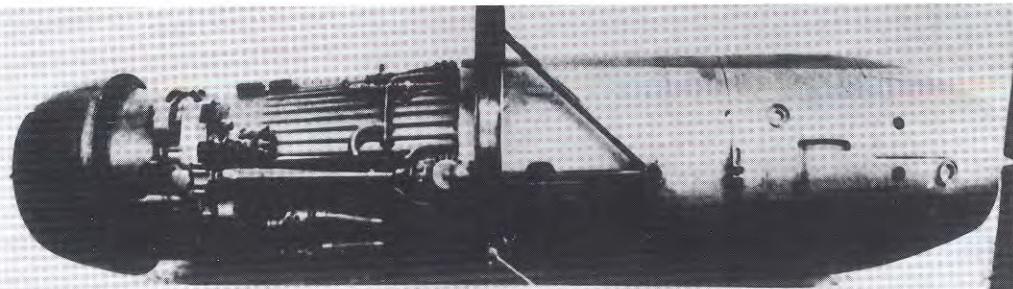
Турбореактивный двигатель Юнкерс 109-012. Имелся только не завершенный до конца макет. Должен был развивать тягу втрое большую, чем у 109-004 В. Его размеры неизбежно предполагали применение корпуса компрессора из листовой стали — иначе вес получался слишком большим
